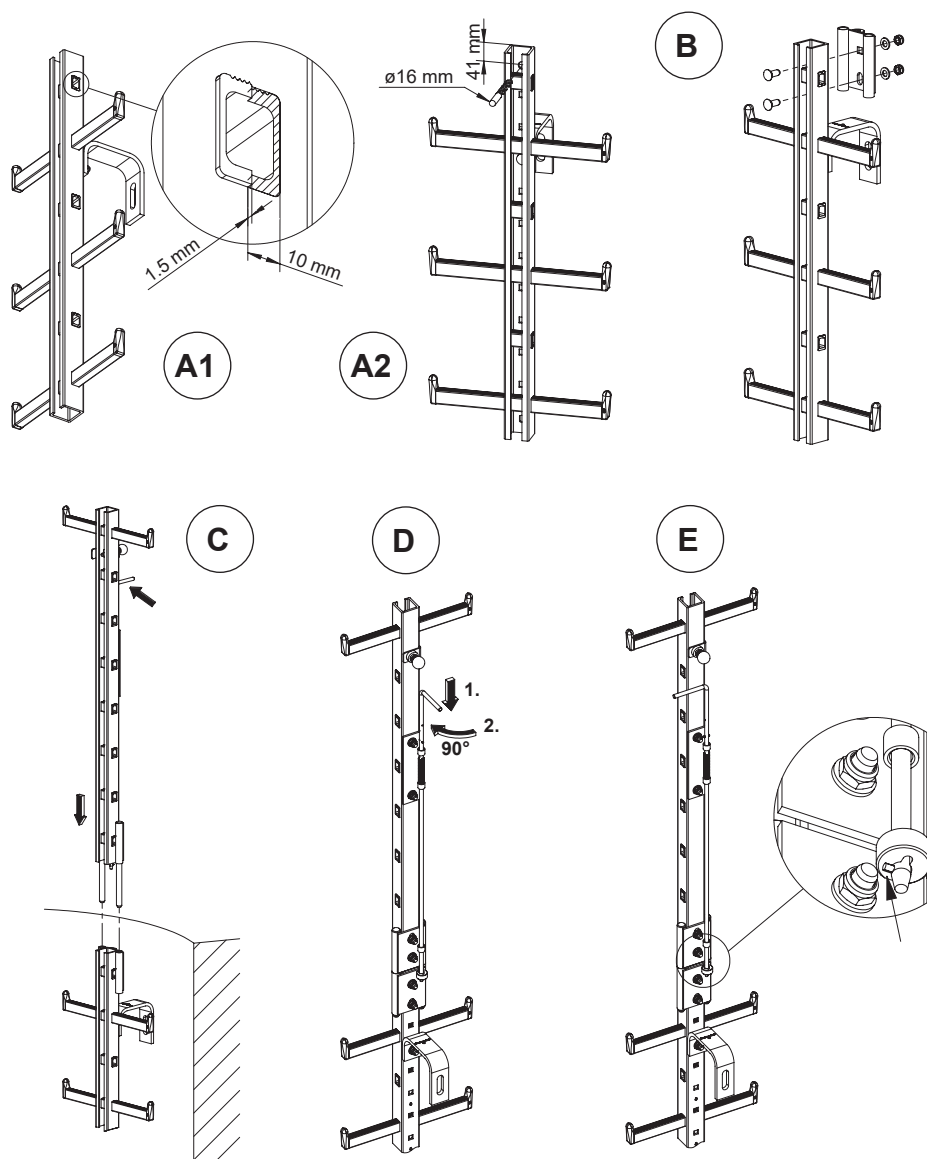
Montaggio dispositivo di ingresso dell'albero:
